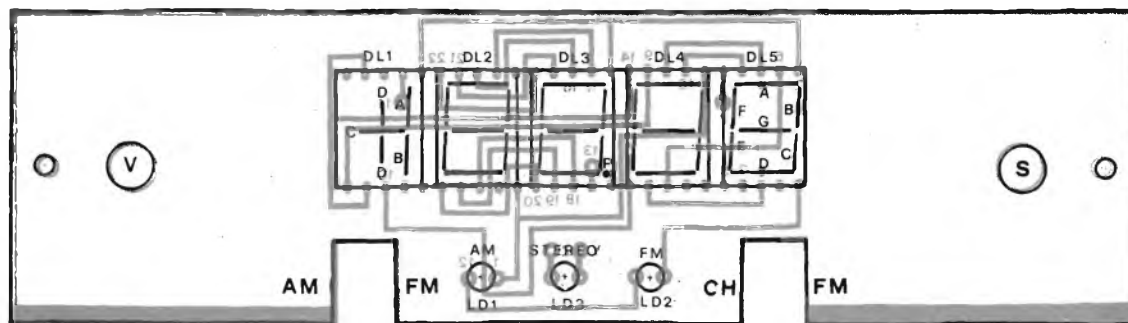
Disposizione dei componenti sul circuito stampato di fig. 3.
